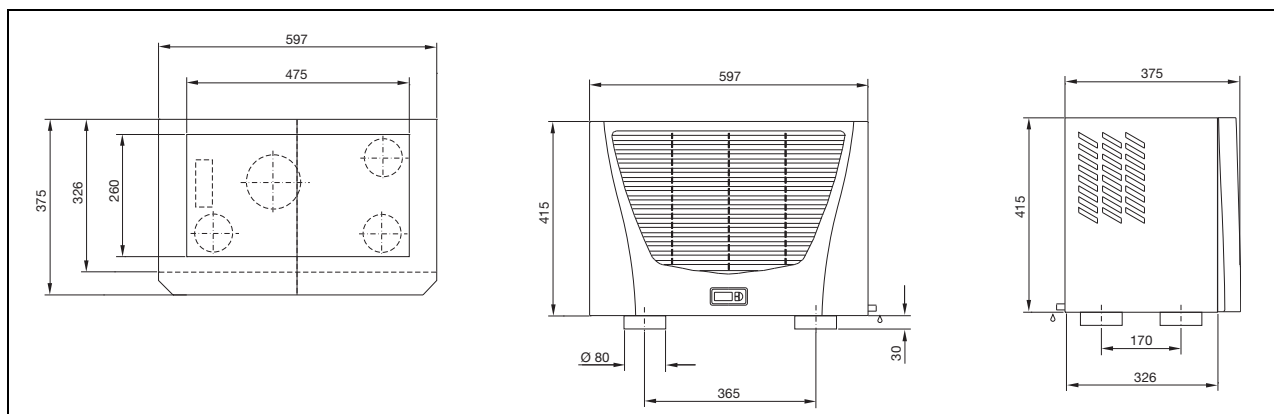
3359.xxx, 3382.xxx påbyggnad
